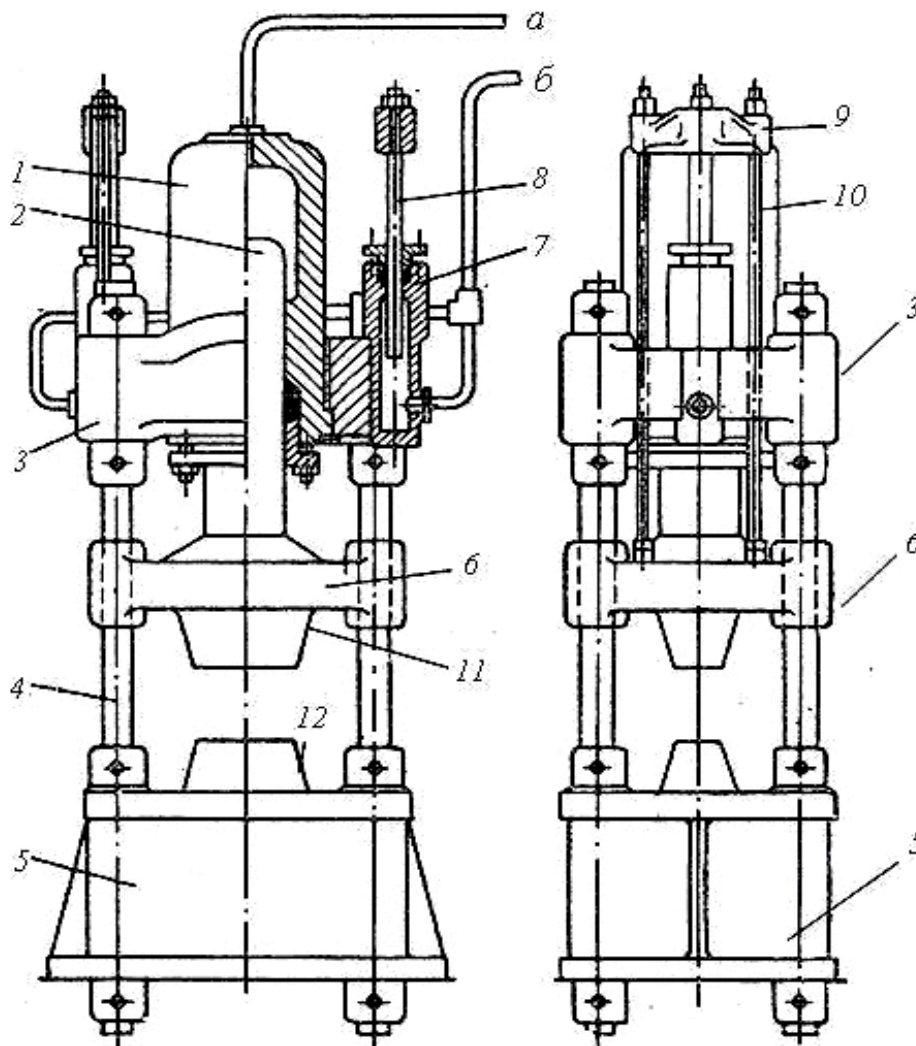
Схема гідравлічного преса: 1 – робочий циліндр; 2 – плунжер; 3 – верхня траверса; 4 – колони; 5 – станина; 6 – рухома траверса; 7 – зворотній циліндр; 8 – підйомні плунжери; 9 – поперечина; 10 – тяги; 11, 12 – бойки
